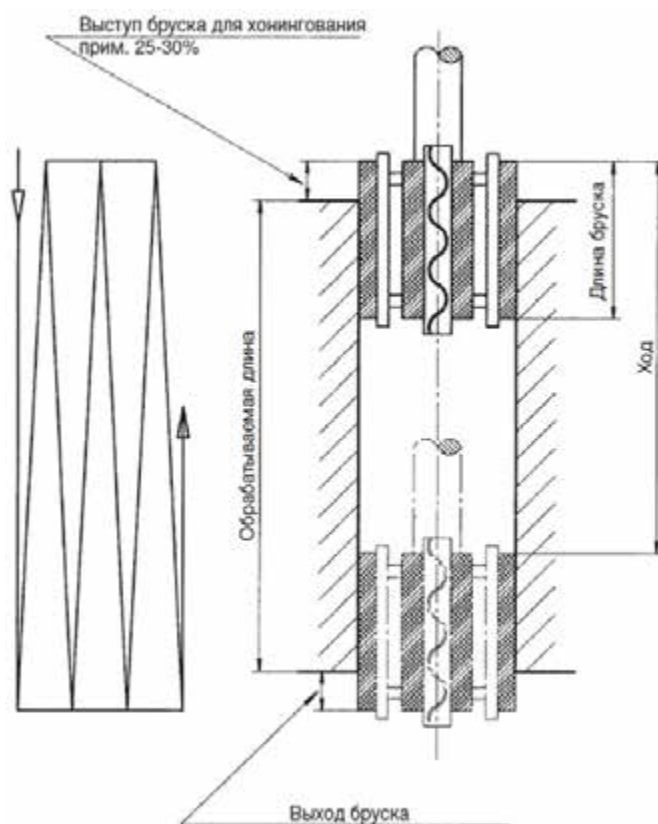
ro-64: Установка хода хона при обработке внутренней поверхности цилиндра, и схема движения хода по рабочей поверхности цилиндра (слева); источник: MSI
